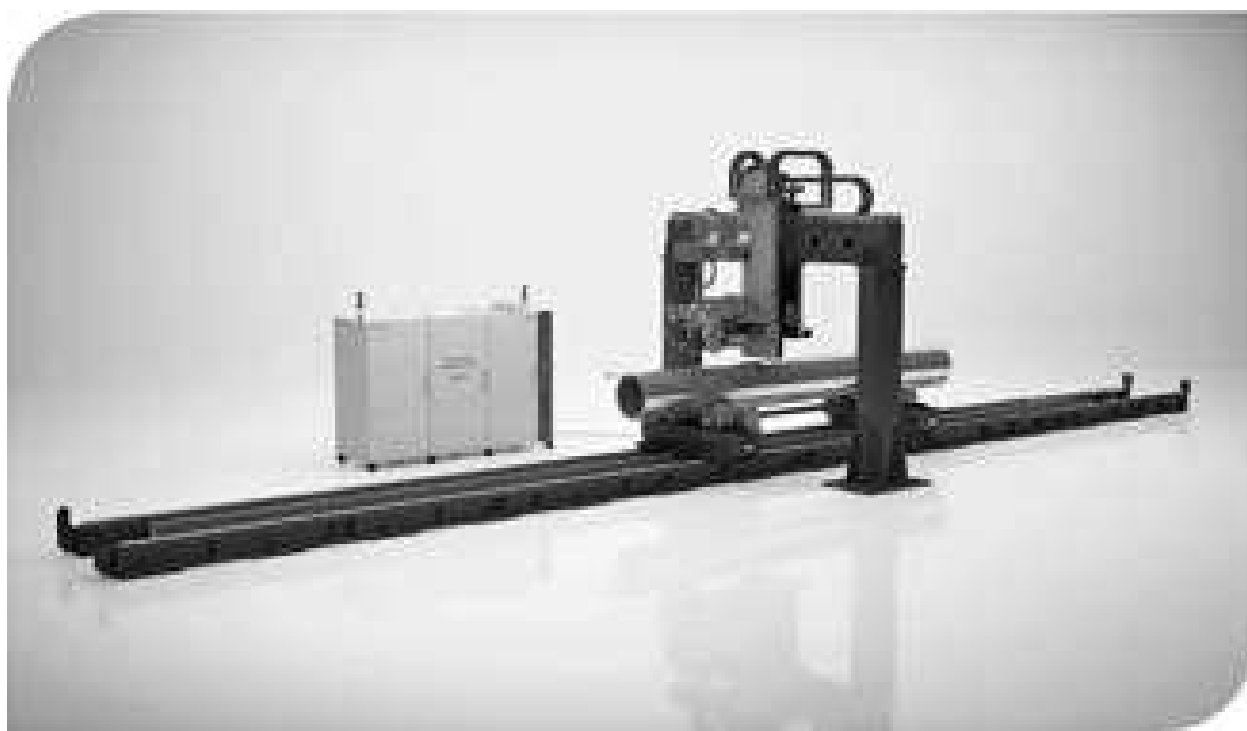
Портальная установка для гибридной лазерно-дуговой сварки
